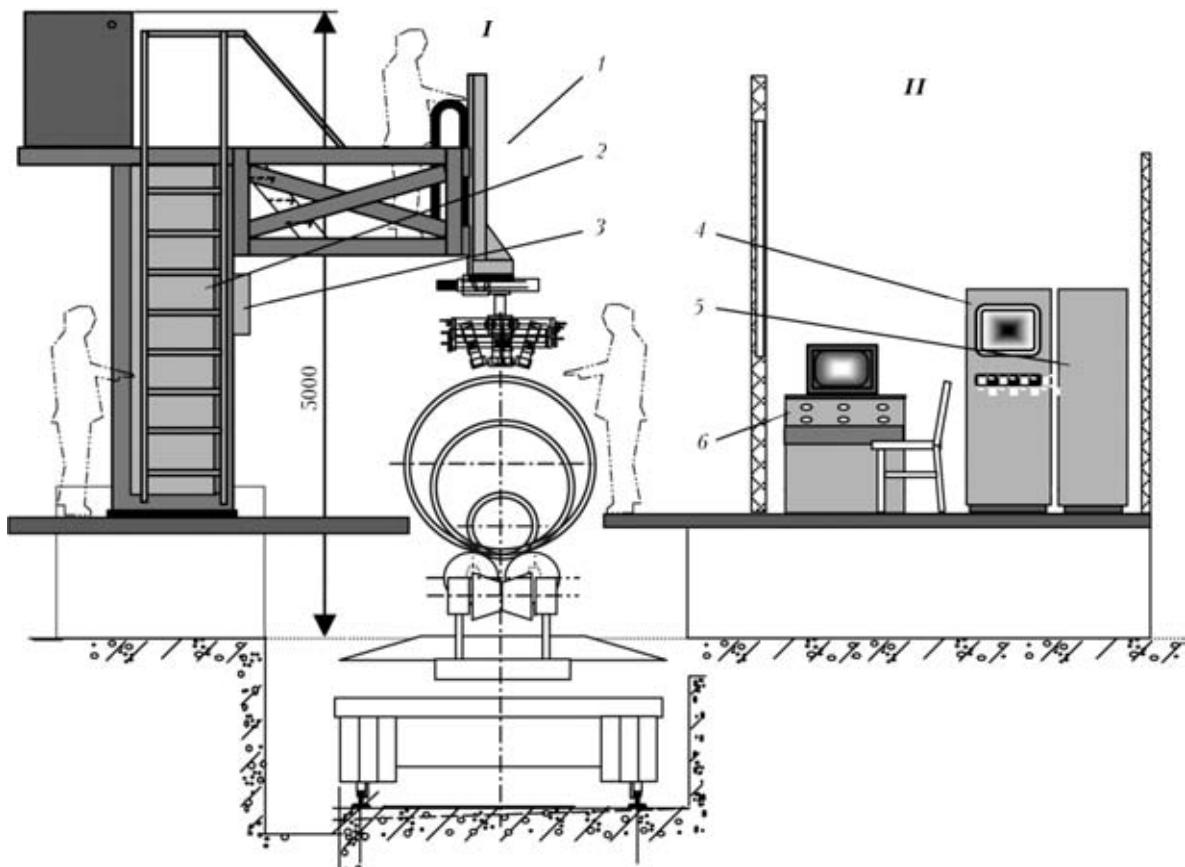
Схема установки НК 360 для АУЗК сварных швов труб диаметром 508...1420 мм: I — размещение установки на линии контроля (вид сбоку); II — кабина оператора; 1 — технологический агрегат АУЗК; 2 — шкаф силовой; 3 — пульт настройки режимов; 4 — многоканальный УЗ дефектоскоп; 5 — шкаф управления; 6 — пульт управления с телемонитором
